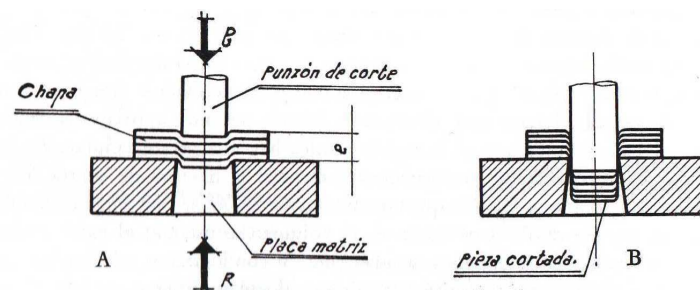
Proceso de corte de la chapa. A) Inicio de corte. B) Final de corte.
